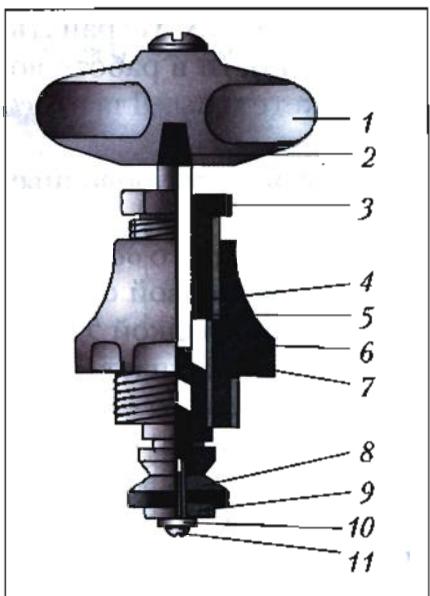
Устройство вентильной головки: 1 – маховичок; 2 – шпиндель; 3 – гайка; 4 – сальник; 5 – шайба; 6 – корпус; 7 – прокладка; 8 – клапан; 9 – прокладка; 10 – шайба; 11 – винт
